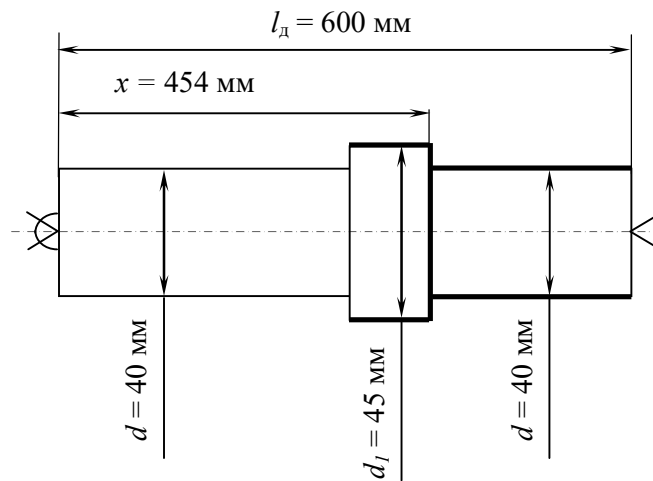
Розрахункова схема для визначення ω_{Σ}
